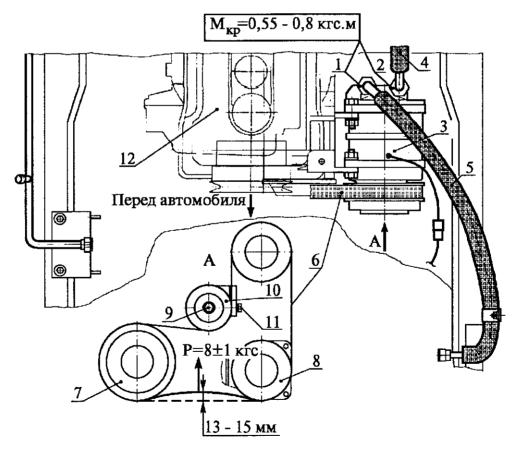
Подсоединение шлангов к компрессору и натяжение ремня привода компрессора:
